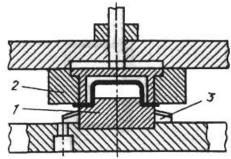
Схема штампа для обрезки фланца: 1 – пуансон; 2 – матрица; 3 – ножи-рассекатели
